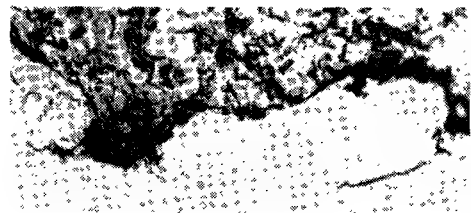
Рельеф поверхности эрозийного разрушения выходной кромки лопатки
